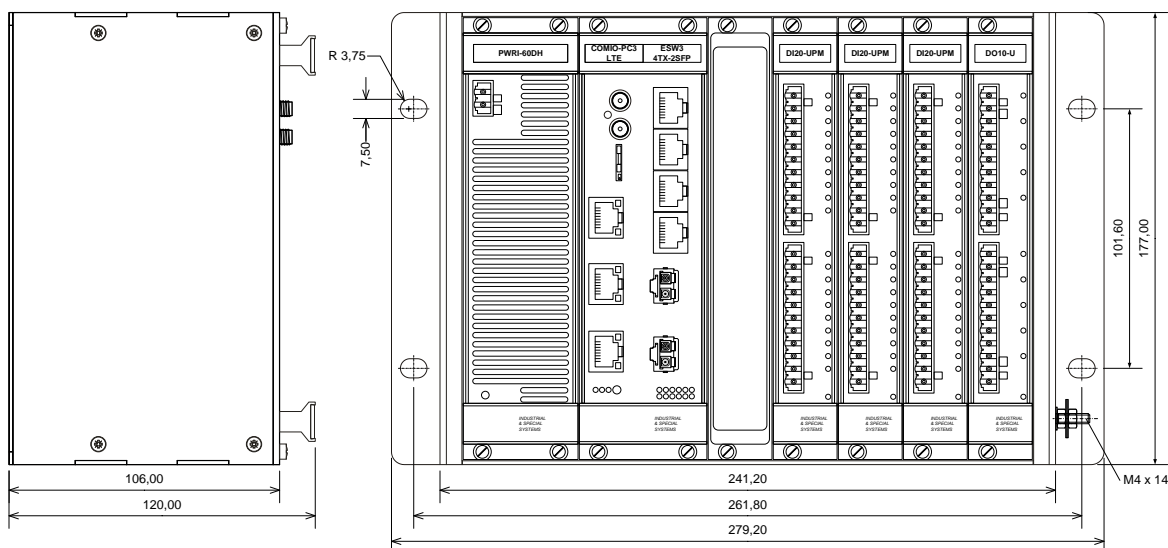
Rozměr vany CASE-3E (jednotky mm)
